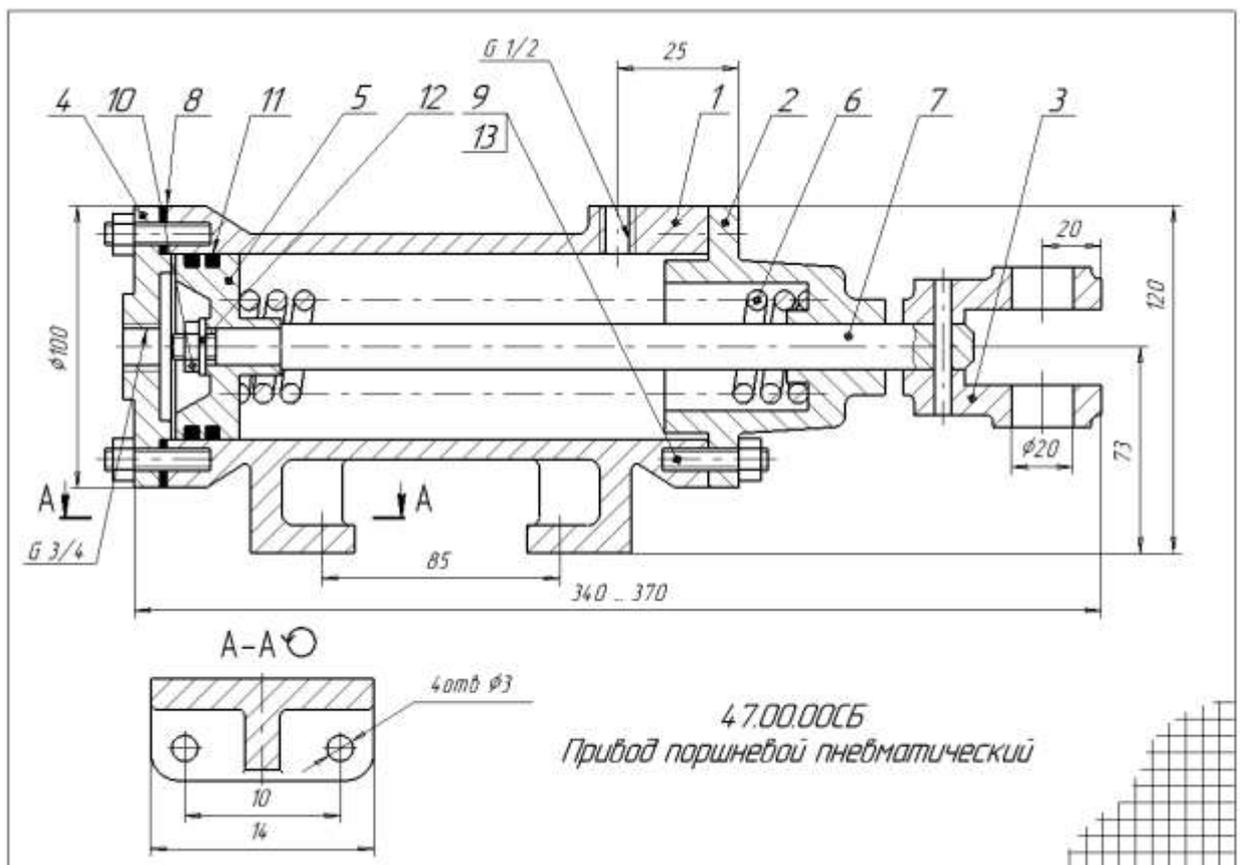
Образец выполнения задания ИГ 9.3 Сборочный чертеж
